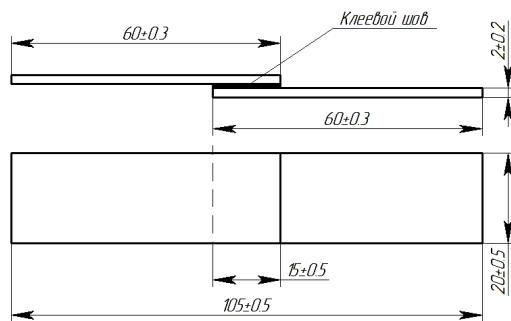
Чертеж сборки для испытания клеевых соединений на сдвиг
